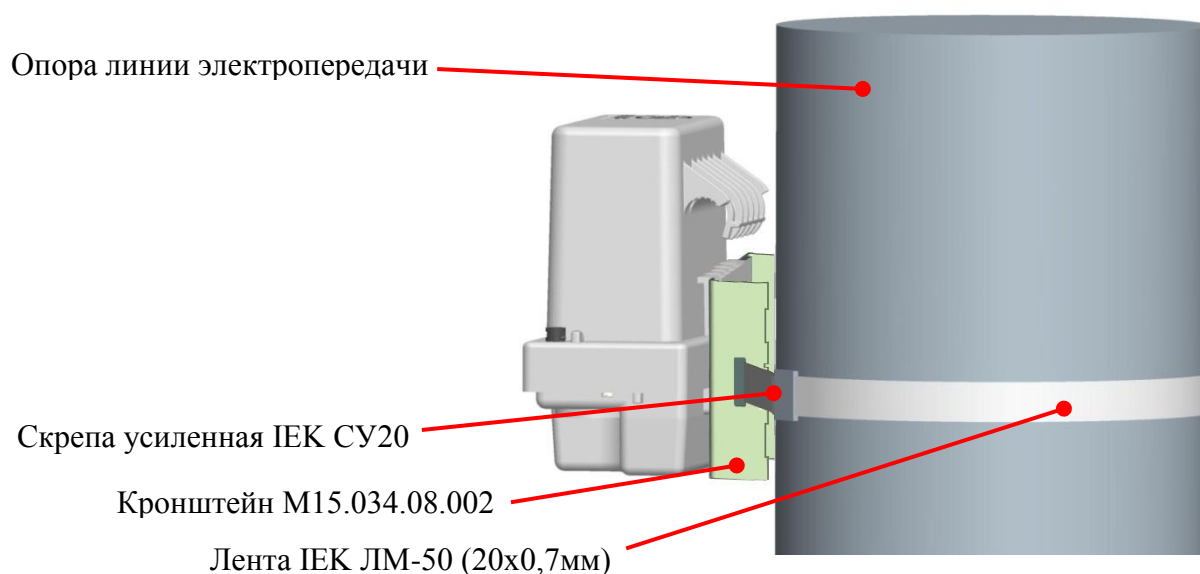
Установка устройства M22.003.00.000-02
